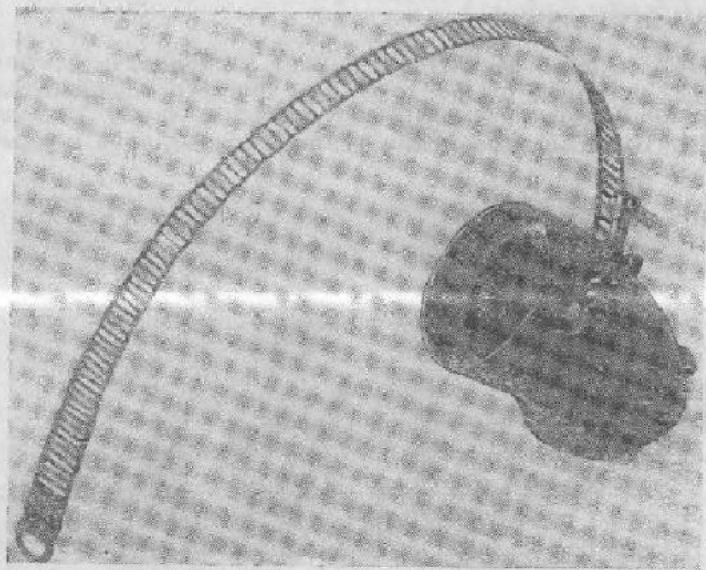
Бугель для обжатия при сборке отвода вентиляции из половин.
